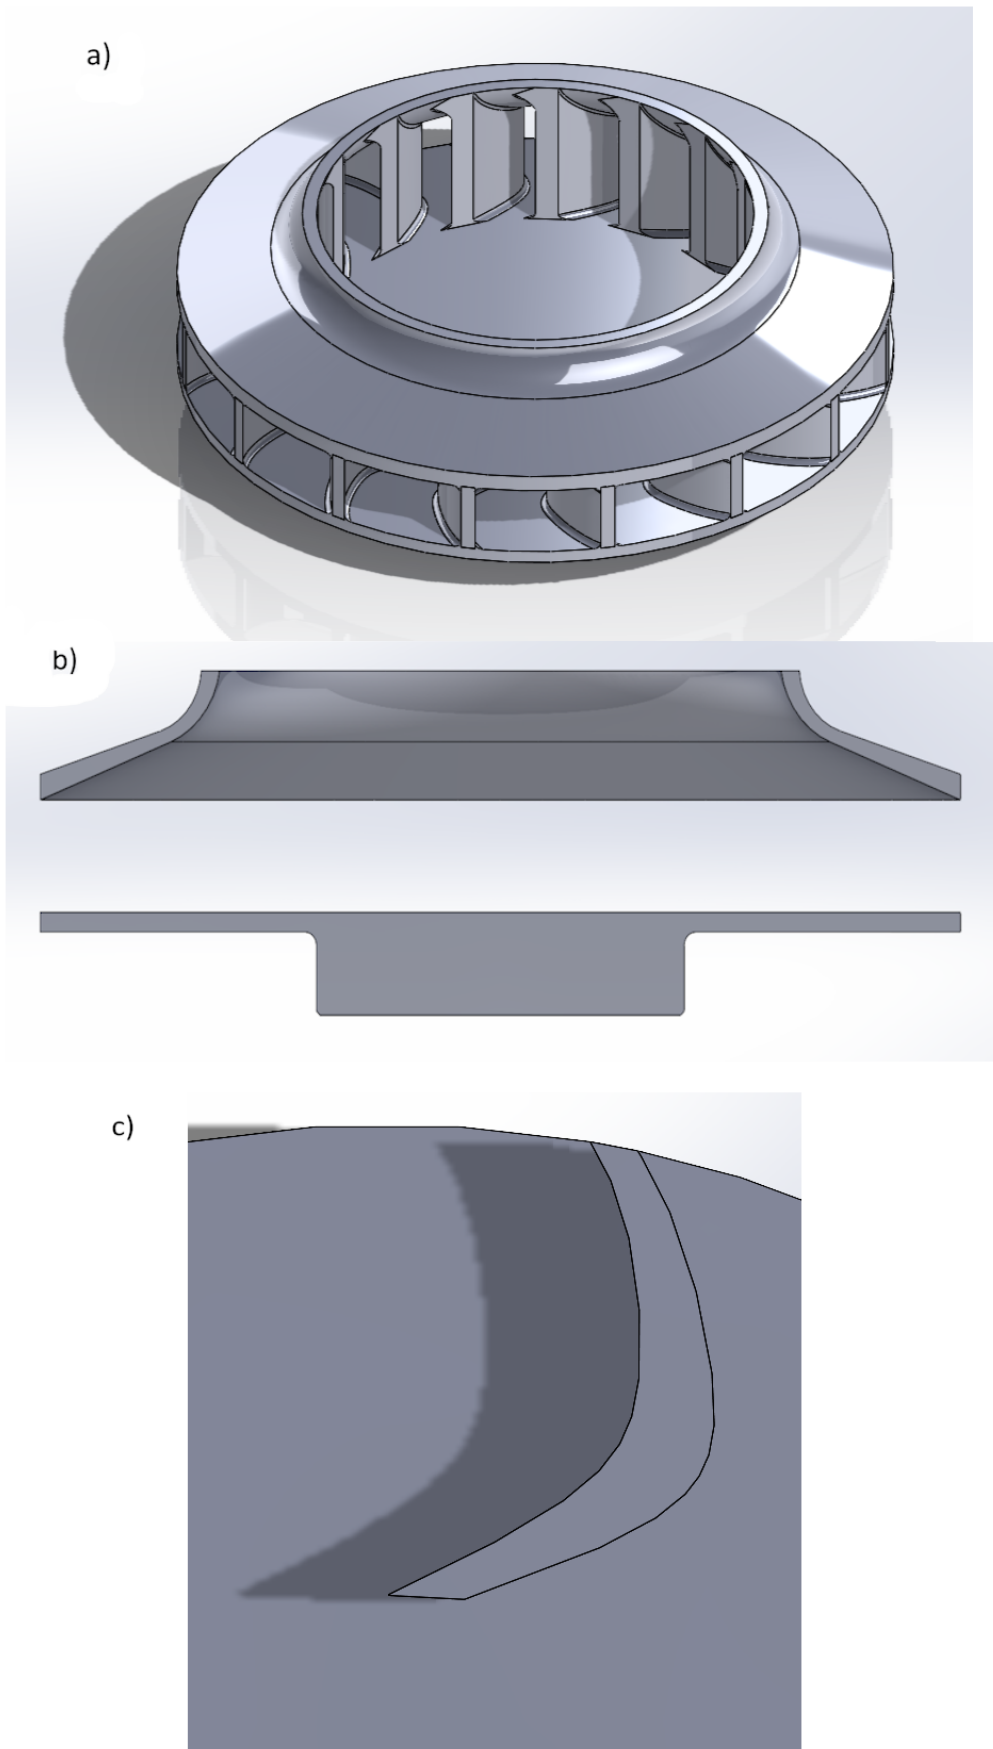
Rotor modelado em *SolidWorks* a) Vista isométrica; b) Pormenor das tampas; c) Pormenor de uma pá
